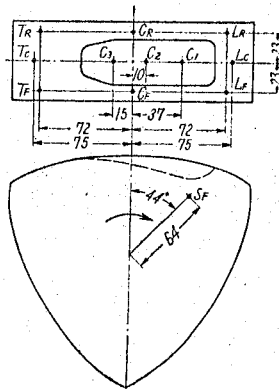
Der Bearbeitungszustand der Seitengehäusegleitfläche und die Schwingungen der Öldichtung (Drehzahl: 4500 U/Min.)
